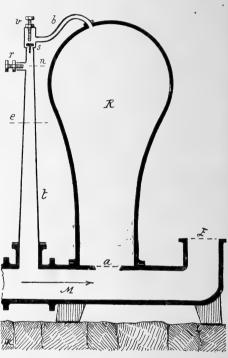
Coupe du bélier hydraulique Vidal-Beaume.
